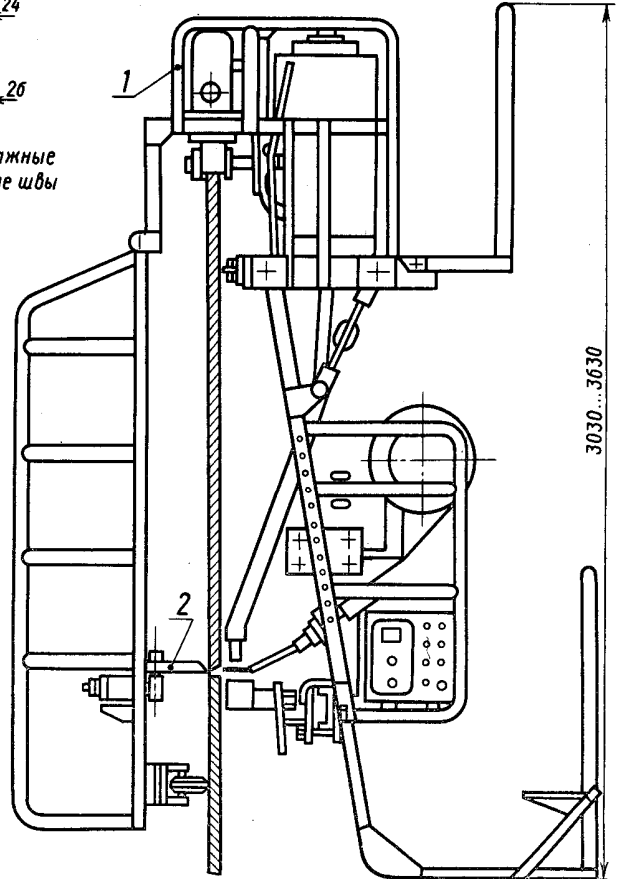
Автоматическая сварка горизонтального шва
